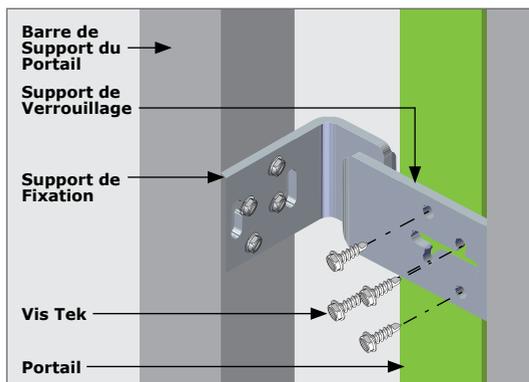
BARRE DE SUPPORT - FIXATIONS
